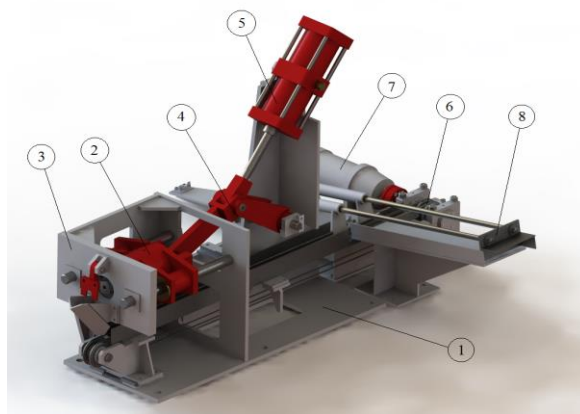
Выходная сторона прошивного стана: 1 – рама; 2 – упорная головка; 3 – опорная плита; 4 – рычажное устройство; 5 – пневмоцилиндр; 6 – цепной транспортер; 7 – привод транспортера; 8 – толкатель
